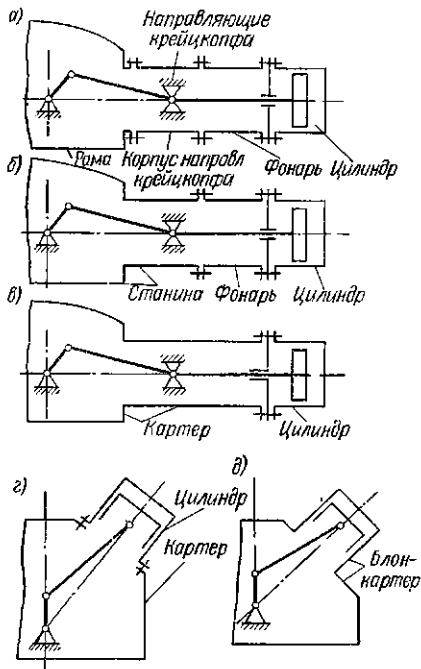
Схемы исполнения корпусных деталей компрессора с базовым элементом: а — рама; б — станина; в, г — картер; д — блок-картер
